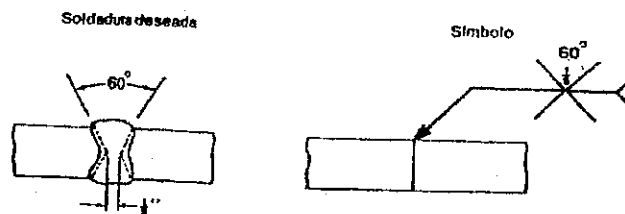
Símbolo de soldadura en el que se representa el 100 % de penetración.
